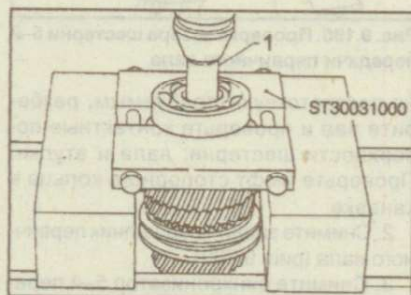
Использование пресса и оправки (1) для снятия заднего подшипника первичного вала
